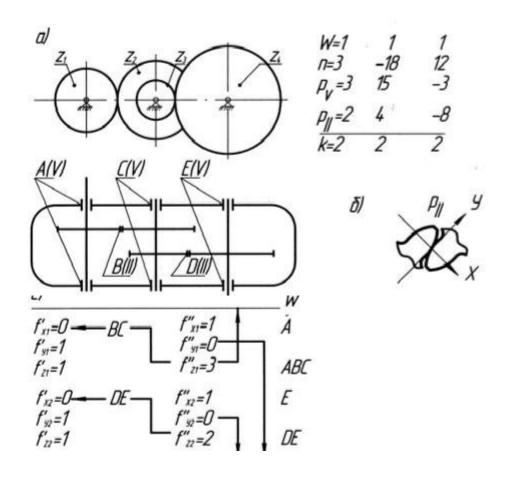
Применяемый редуктор: а – кинематическая схема; б – контакт зубьев первой ступени редуктора; с – таблица распределения подвижностей в кинематических парах
